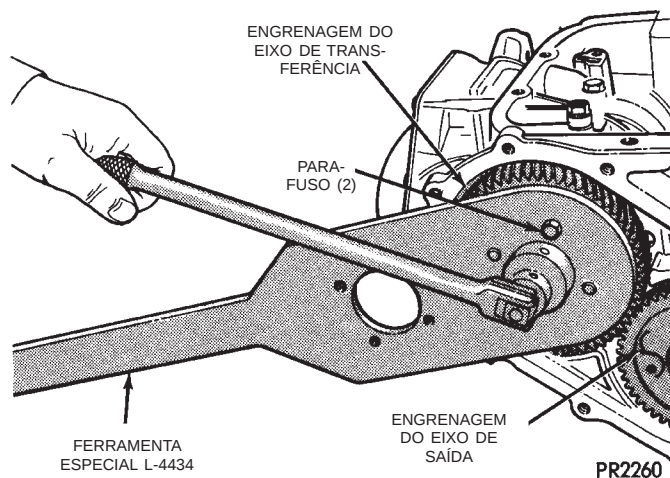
Remoção da Porca de Retenção da Engrenagem do Eixo de Transferência
